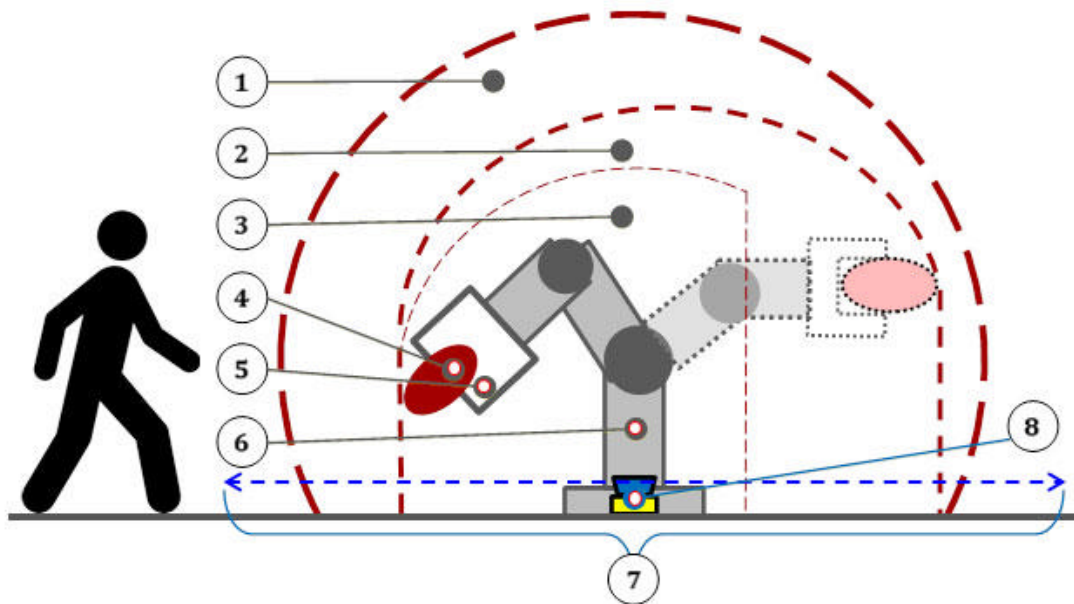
Приміщення для роботизованого зварювального обладнання (Robotics Industries Association, RIA): 1 - максимальний робочий простір; 2 - обмежений простір; 3 - робочий простір; 4 заготовка; 5 - кінцева точка; 6 – маніпулятор; 7 - охоронний простір; 8 захисний пристрій або бар'єр
